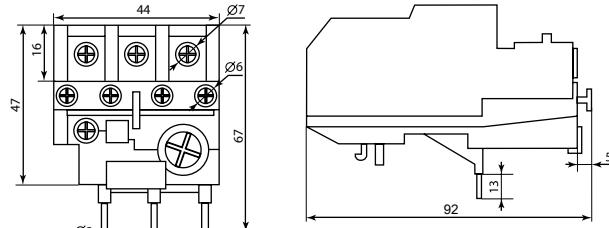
Габаритные и установочные размеры реле РТИ-1302...РТИ-1322
